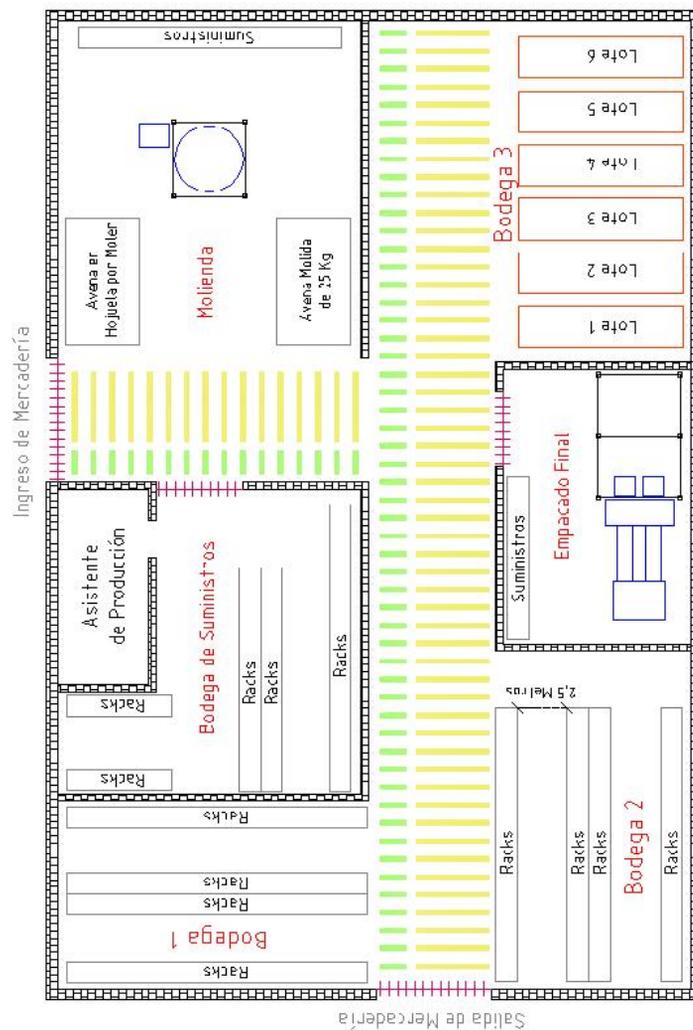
LAYOUT PROPUESTO PARA LA PLANTA
